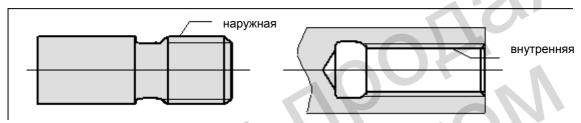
Наружная/внутренняя резьба на примере цилиндрической резьбы
